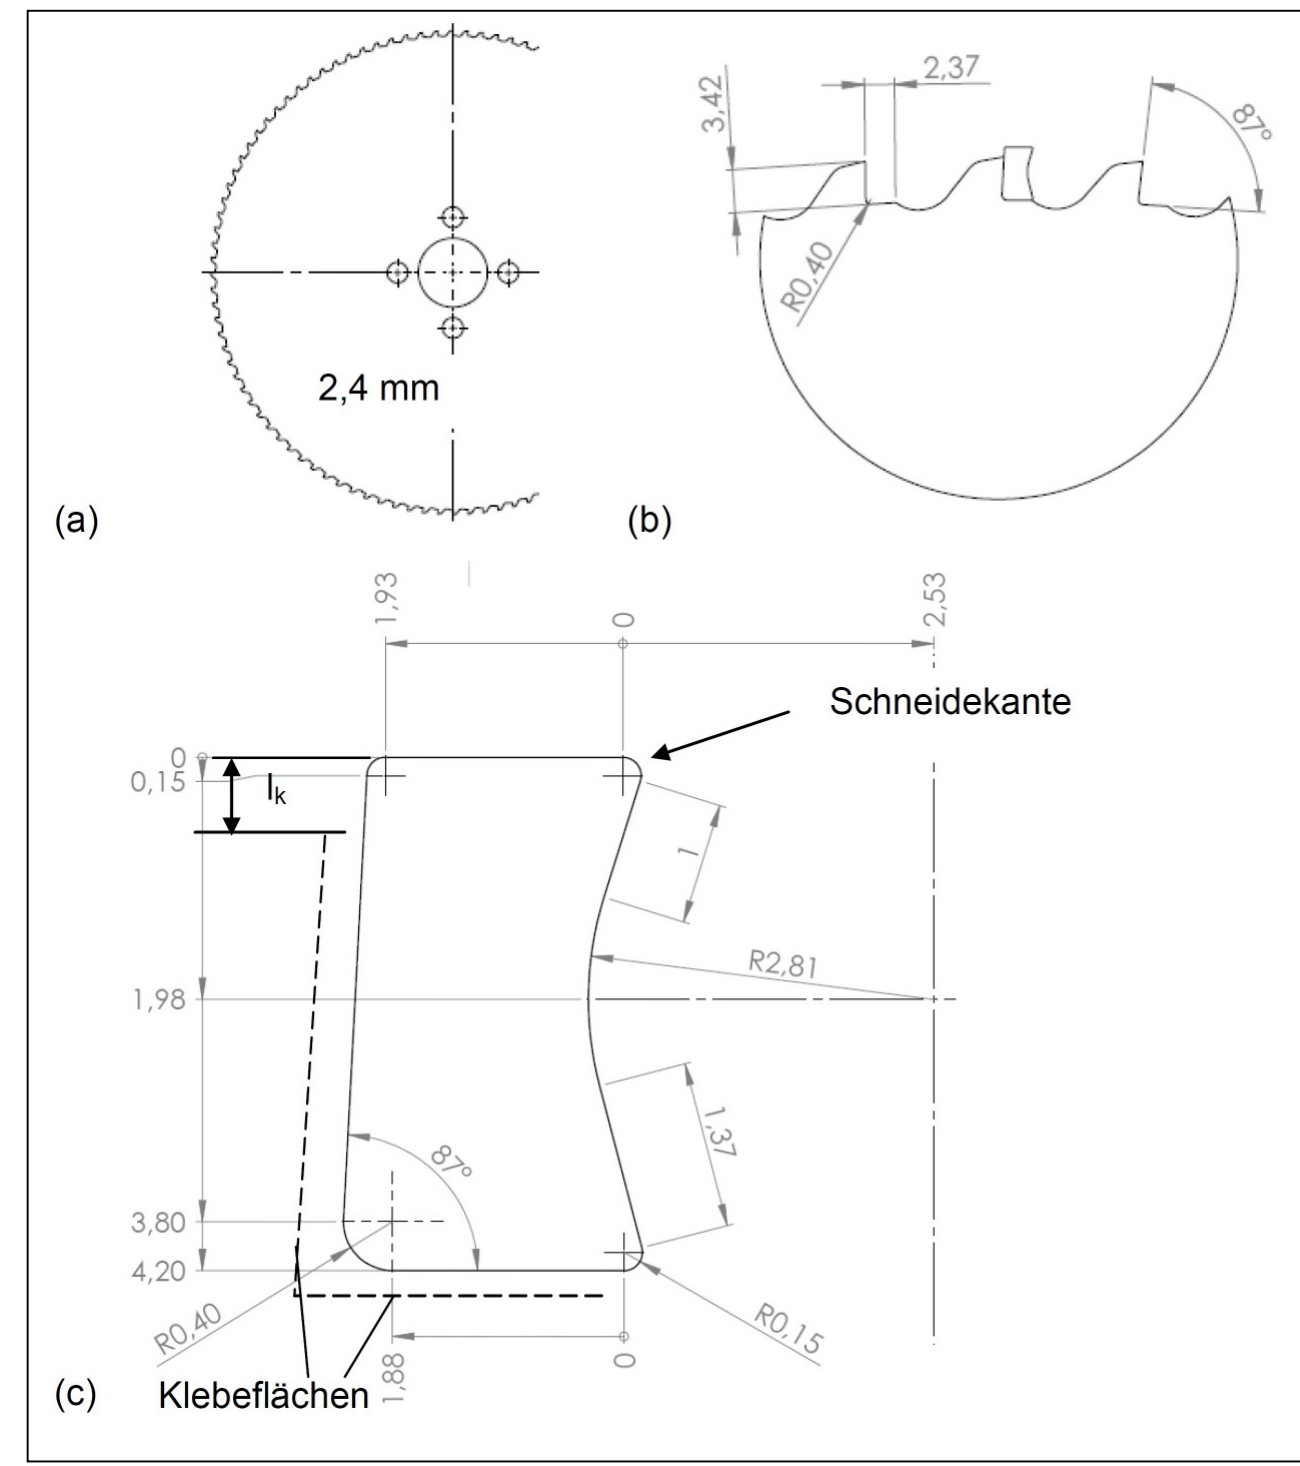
Entwurf Fa. Kampmann: (a) Stamblatt aus Werkzeugstahl 80CrV2, (b) Detail Stamblatt mit Sägezahn, (c) Zahn [2]
